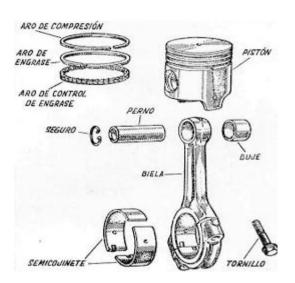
Elementos integrantes del conjunto pistón-biela. Fuente. (Brian, 2011).
